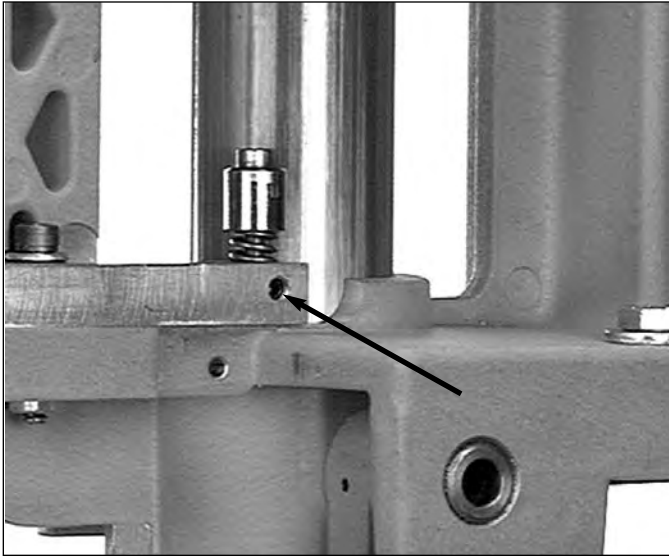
[Figure 7] Diese Setzschraube [set screw] wird vor dem Auswechseln des Zündhütchen-Behälters und -Stiftes [primer cup and pin] gelockert. (Siehe Pfeil)
